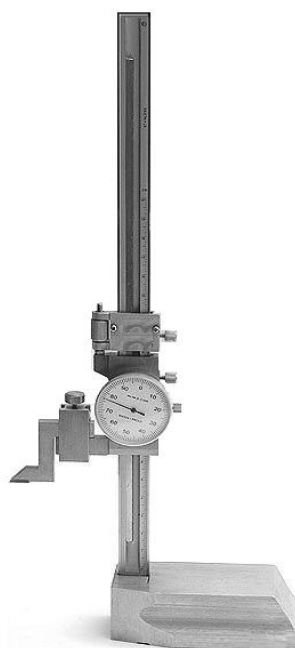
Общий вид штангенрейсмаса ШРК
